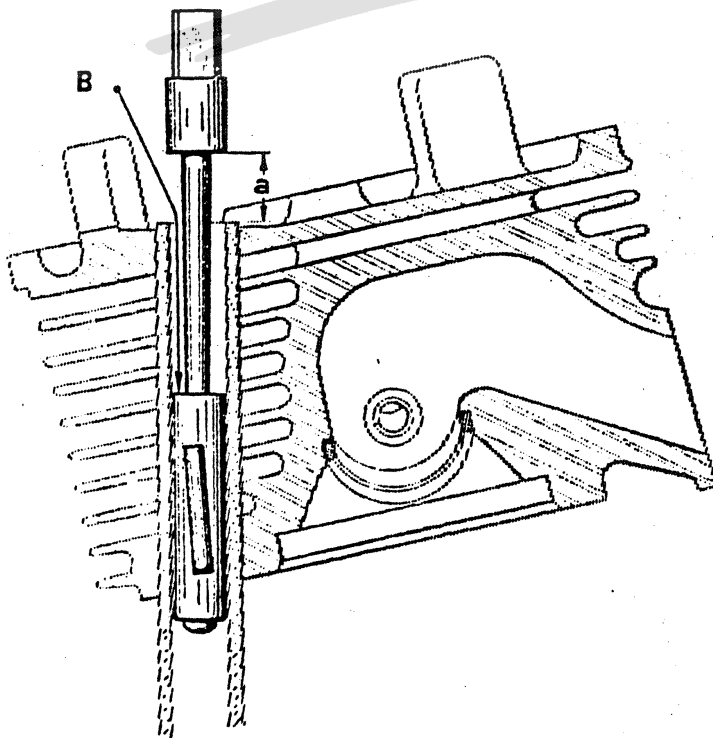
Arbeiten mit dem Spezialwerkzeug 1605-YA zum Einbau der Stosstangenrohre in den Zylinderkopf
